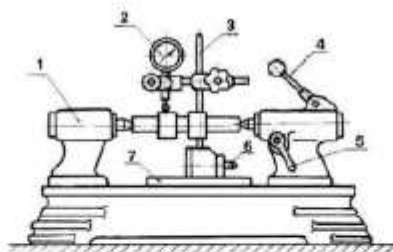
Пристрій для тестування деталей на кругові відхилення на обертових центрах: 1 - точка обертання; 2 - годинниковий індикатор; 3 - опора; 4 - ручка; 5 - хомут; 6 - перемикач управління магнітом; 7 - робоча поверхня.
